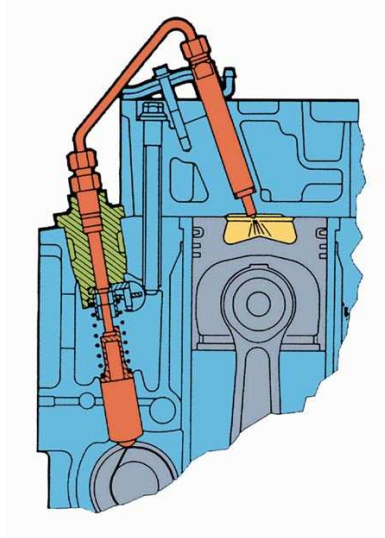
Palivová soustava motoru se sdruženými vstřikovači [5]
